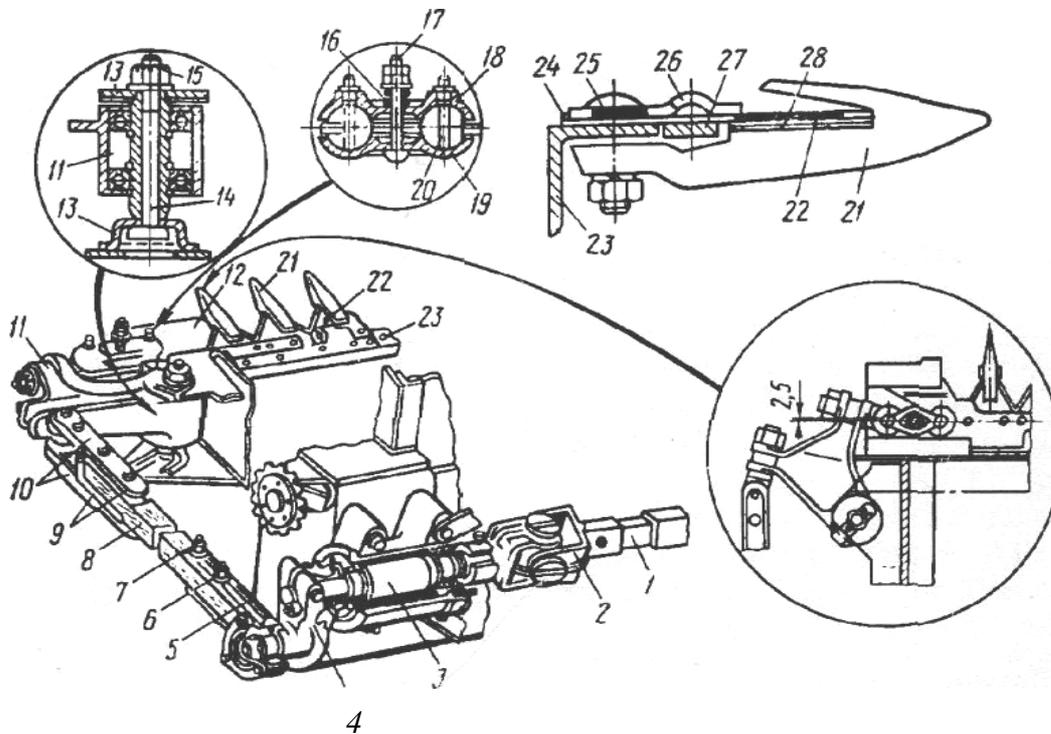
Режущий аппарат и механизм привода ножа комбайна «Нива»:
